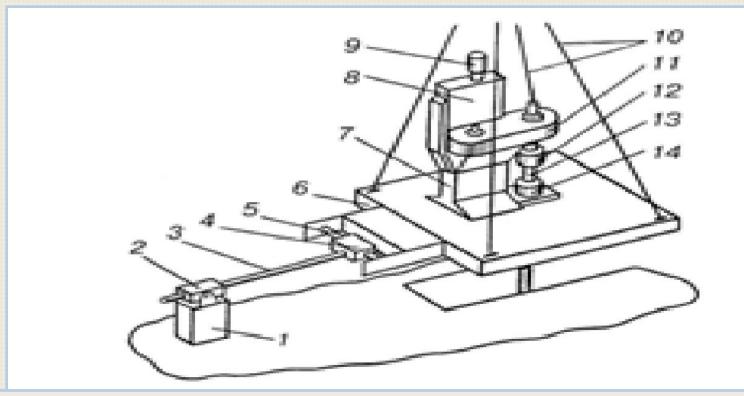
Буровой вращатель на колонне труб: 1 — стойка; 2 — каретка; 3 — продольная штанга; 4 — каретка; 5 — поперечная штанга; 6 — рабочая площадка; 7 — станина; 8 — коробка скоростей; 9 — гидромотор; 10 — тросы; 11 — редуктор; 12 — зажимный патрон; 13 — буровые трубы; 14 — патрон труборазворота
